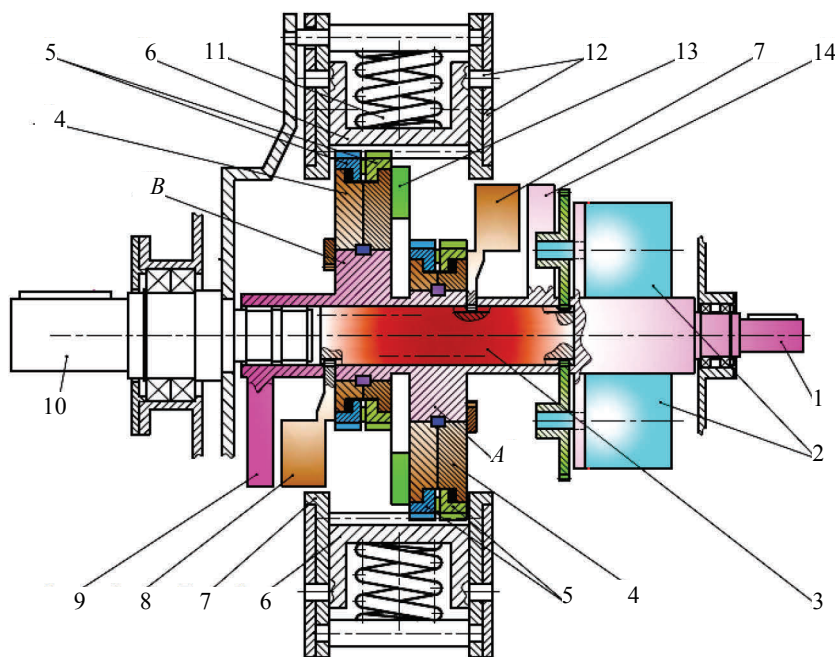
Схема планетарной плавнорегулируемой передачи с циклоидально-цевочным зацеплением: 1 – ведущий вал с эксцентриками A и B; 2 – шаговый двигатель; 3 – промежуточное управляющее зубчатое колесо; 4 – эксцентричная втулка с зубчатым колесом 4', находящимся в зацеплении с зубчатым колесом 3; 5 – зубчатые венцы сателлита; 6 – зубчатый сектор центрального зубчатого колеса; 7 – корпус центрального зубчатого колеса; 8 – противовес эксцентричной втулки; 9 – противовес эксцентрика B; 10 – выходной вал; 11 – пружина силового замыкания зубьев сателлита и секторов центрального зубчатого колеса; 12 – многопоточный кулачковый механизм центрального зубчатого колеса; 13 – механизм фиксации сателлитов от вращения относительно собственной оси; 14 – противовес эксцентрика A
